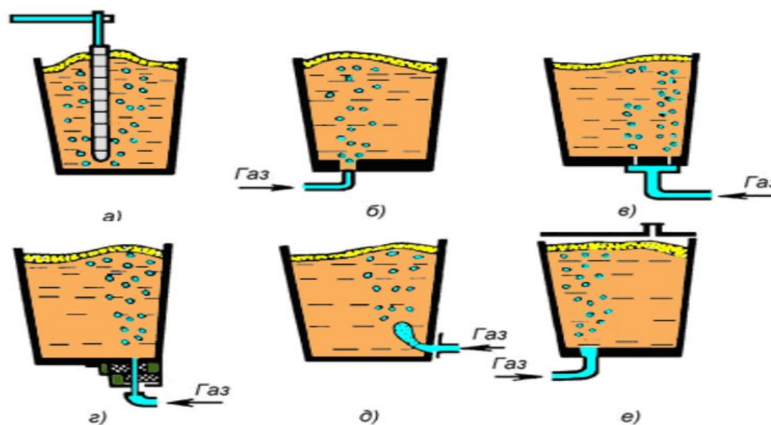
Способы продувки металла в ковше: а – через погружаемую фурму; б – через пористый блок; в – через пористые швы в днище; г – через шиберный затвор; д – через боковую стенку ковша; е – способ SAB
